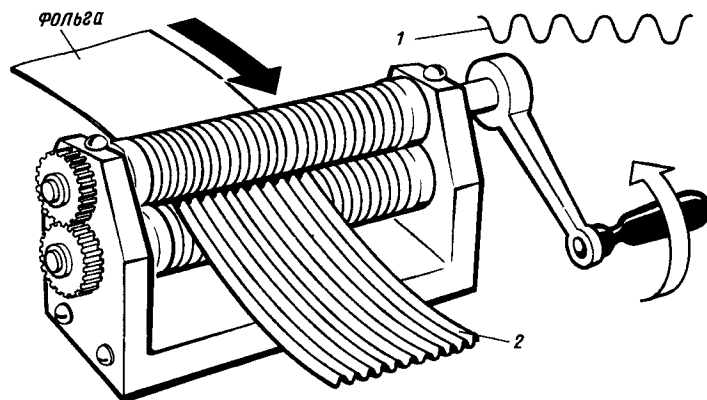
«Прокатный стан» для изготовления гофрированной обшивки
